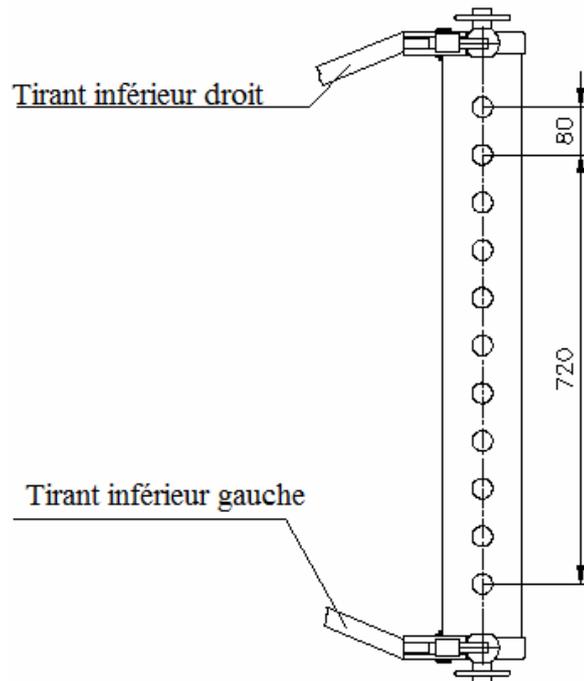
Schéma d'installation du dispositif TSU-1 (traverse)
